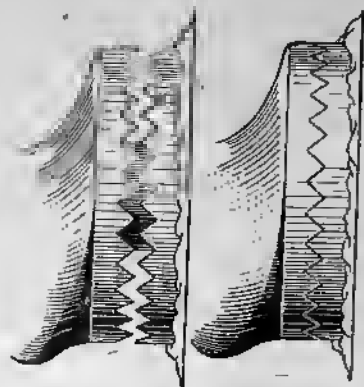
Зубчатое зацепление кривошипа ленивца с кронштейном на корпусе
